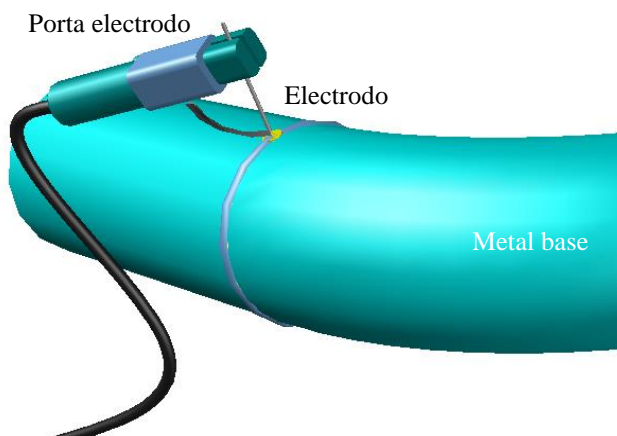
Esquema del proceso soldadura SMAW.
